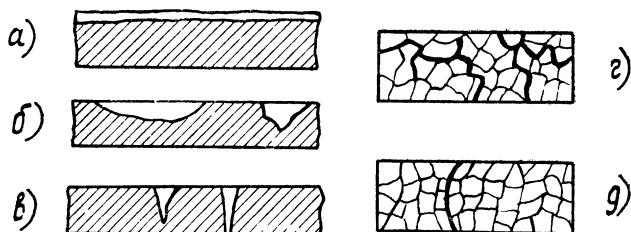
Виды коррозионных повреждений котельного металла:
